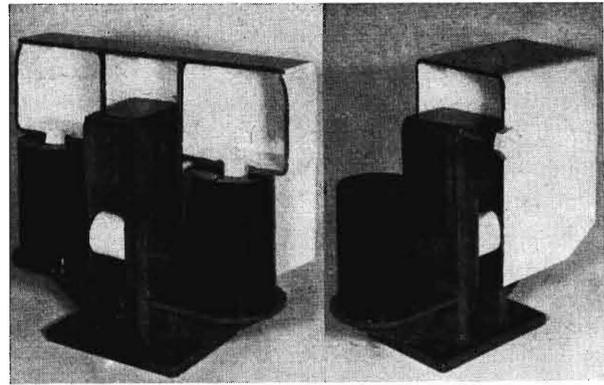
Baugruppe „Gummifederung“ mit Längs- und Querschnitt des Oberkastens. Eine einzige M-16-Schraube verhindert ein Auseinanderfallen der Baugruppe.
